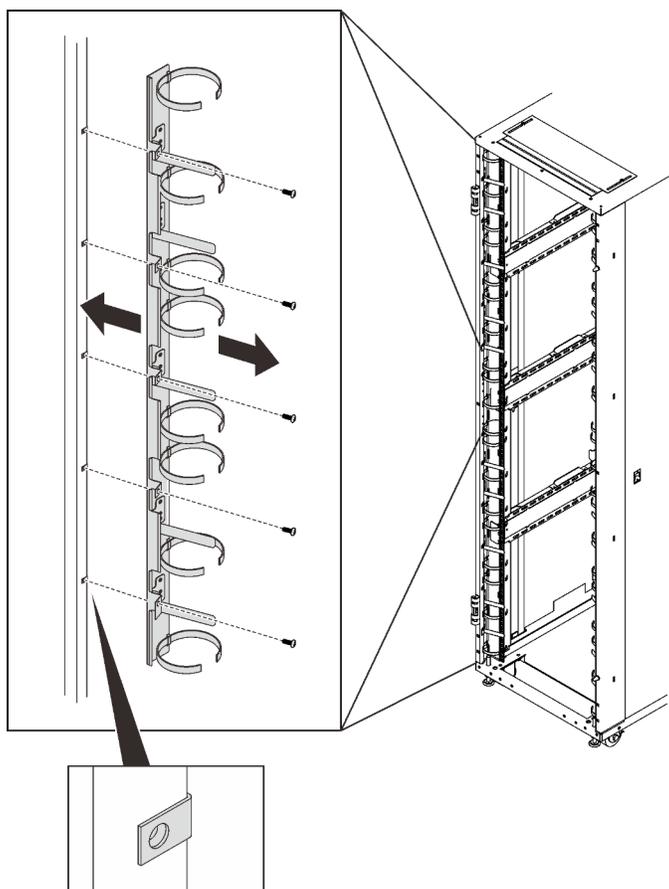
Removendo um suporte de gerenciamento de cabos frontais 21U
